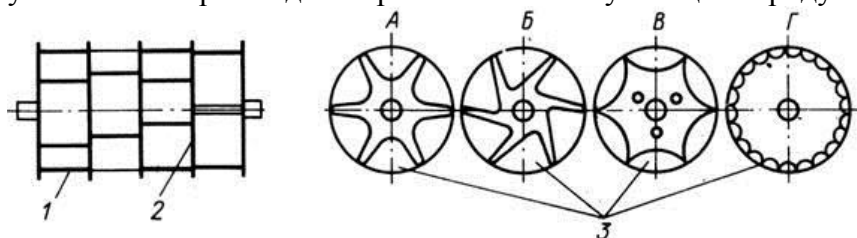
41. Схема рабочего органа барабанного дозатора ДП-1: 1 – барабан; 2 – дозирующий диск; 3 – звездочки
